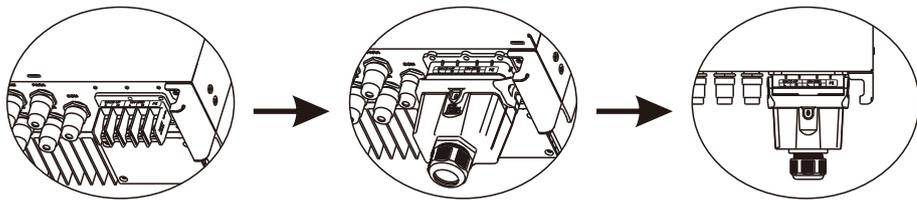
Installazione dei cavi AC per l'inverter
